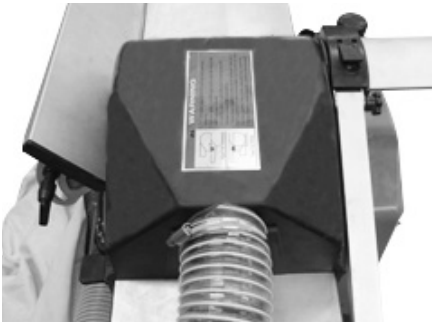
Instalação da caixa coletora de pó sobre as facas
